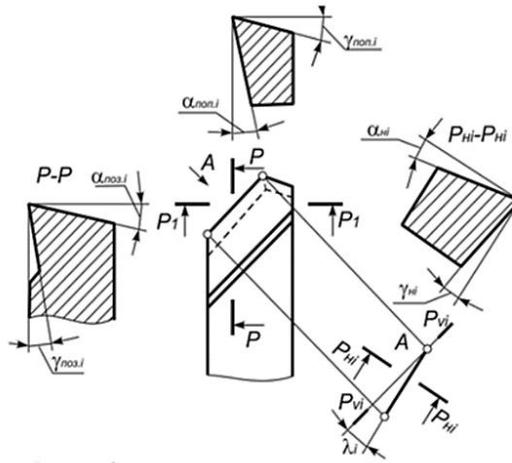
Геометричні параметри ріжучої частини токарного різця [1]
